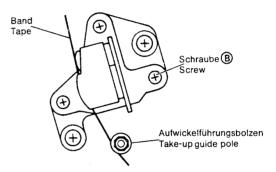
Aufwickelführungsbolzen Fig. 4-8 Take-up guide pole
